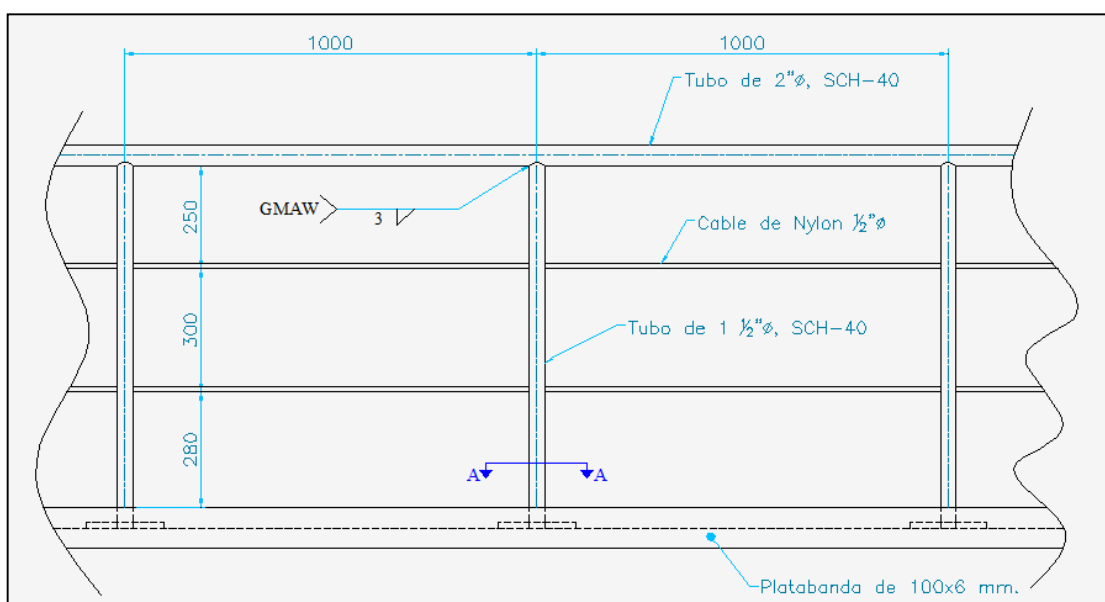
Vista frontal de la baranda de la segunda cubierta.
